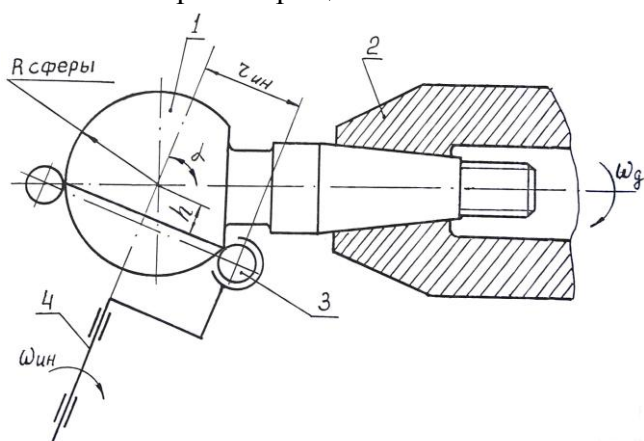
Схема планетарной обкатки неполных сферических поверхностей шариковым обкатником: 1 – заготовка, 2 – шпиндель заготовки, 3 – деформирующие элементы (шарики) обкатника, 4 – шпиндель обкатника
